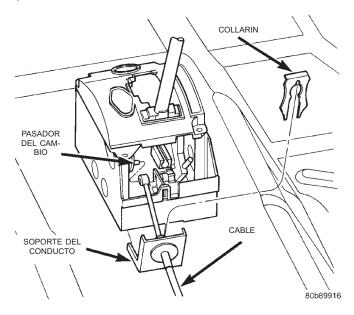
Cable de la palanca de cambios en el conjunto del cambiador de suelo
